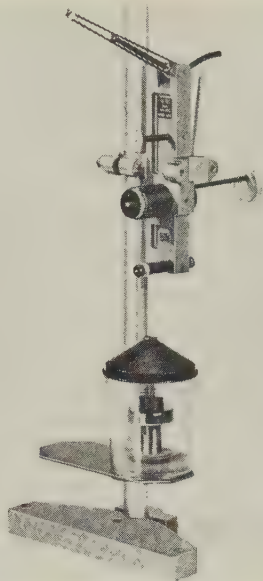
Drahtabspulgerät für Wickelmaschinen.
